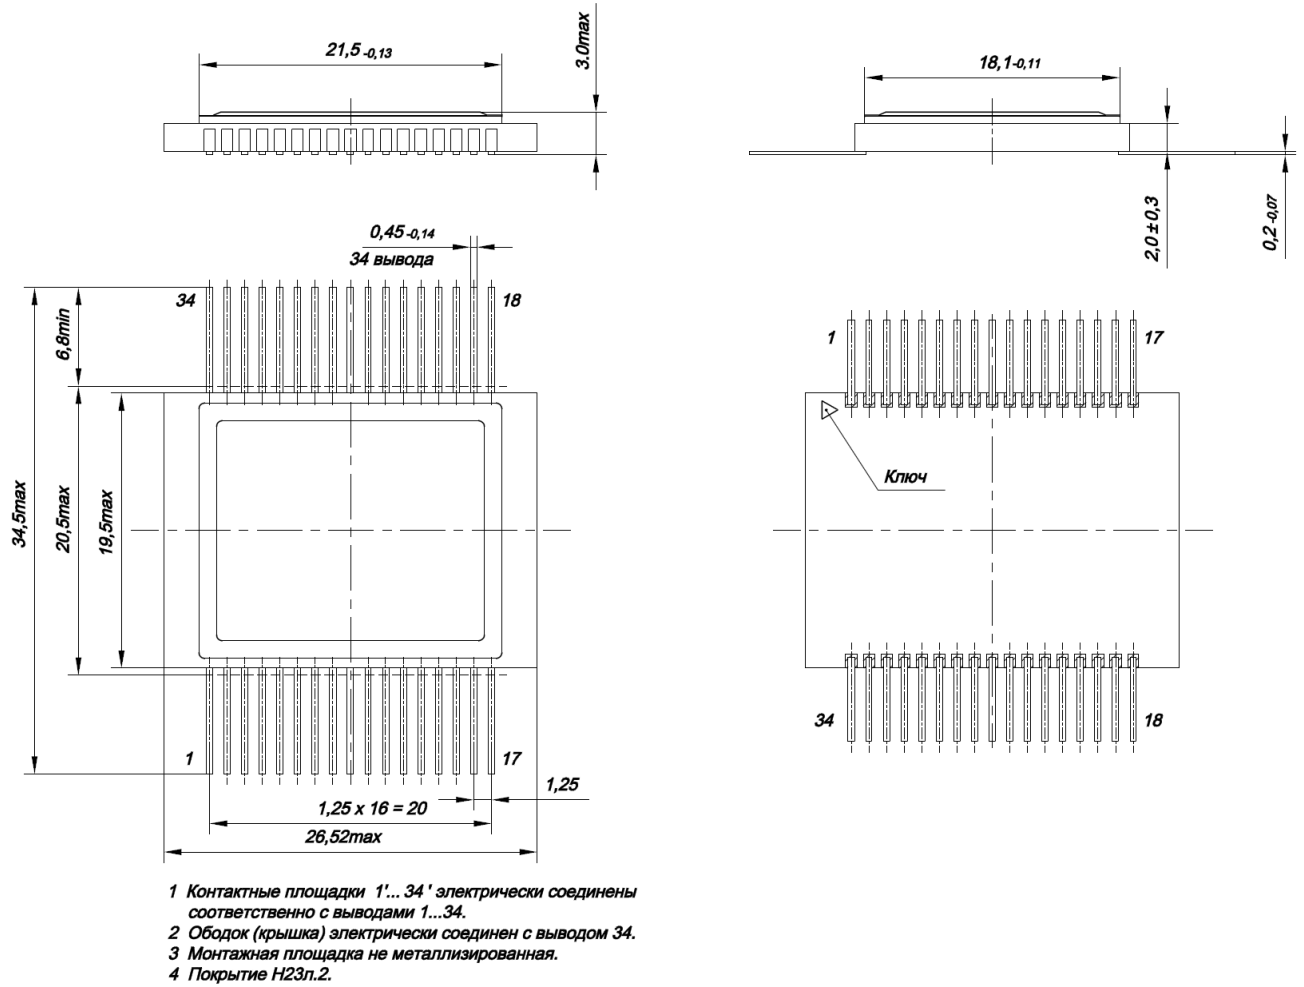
Габаритный чертеж корпуса 4137.34-3.
